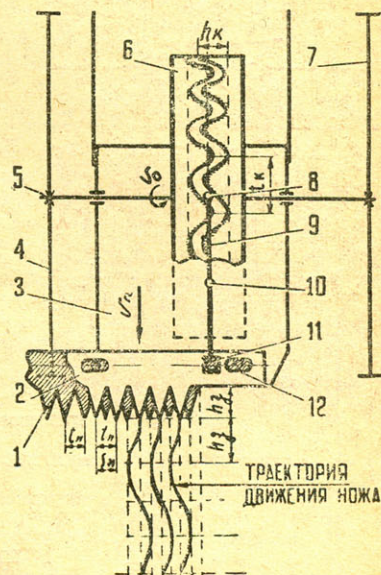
Принципиальная схема газонной косилки: 1 — противорежущая (зубчатая) гребенка; 2 — нож; 3 — плита (рама); 4, 7 — ходовые колеса; 5 — вал ходовых колес; 6 — кулачковый барабан; 8, 11 — ролики двуплечего рычага; 9 — двуплечий рычаг; 10 — ось двуплечего рычага; 12 — направляющая стойка.
